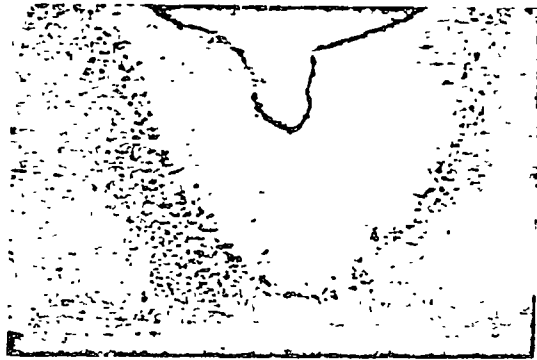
5 X.—Rechupe en el cráter de una soldadura por arco
